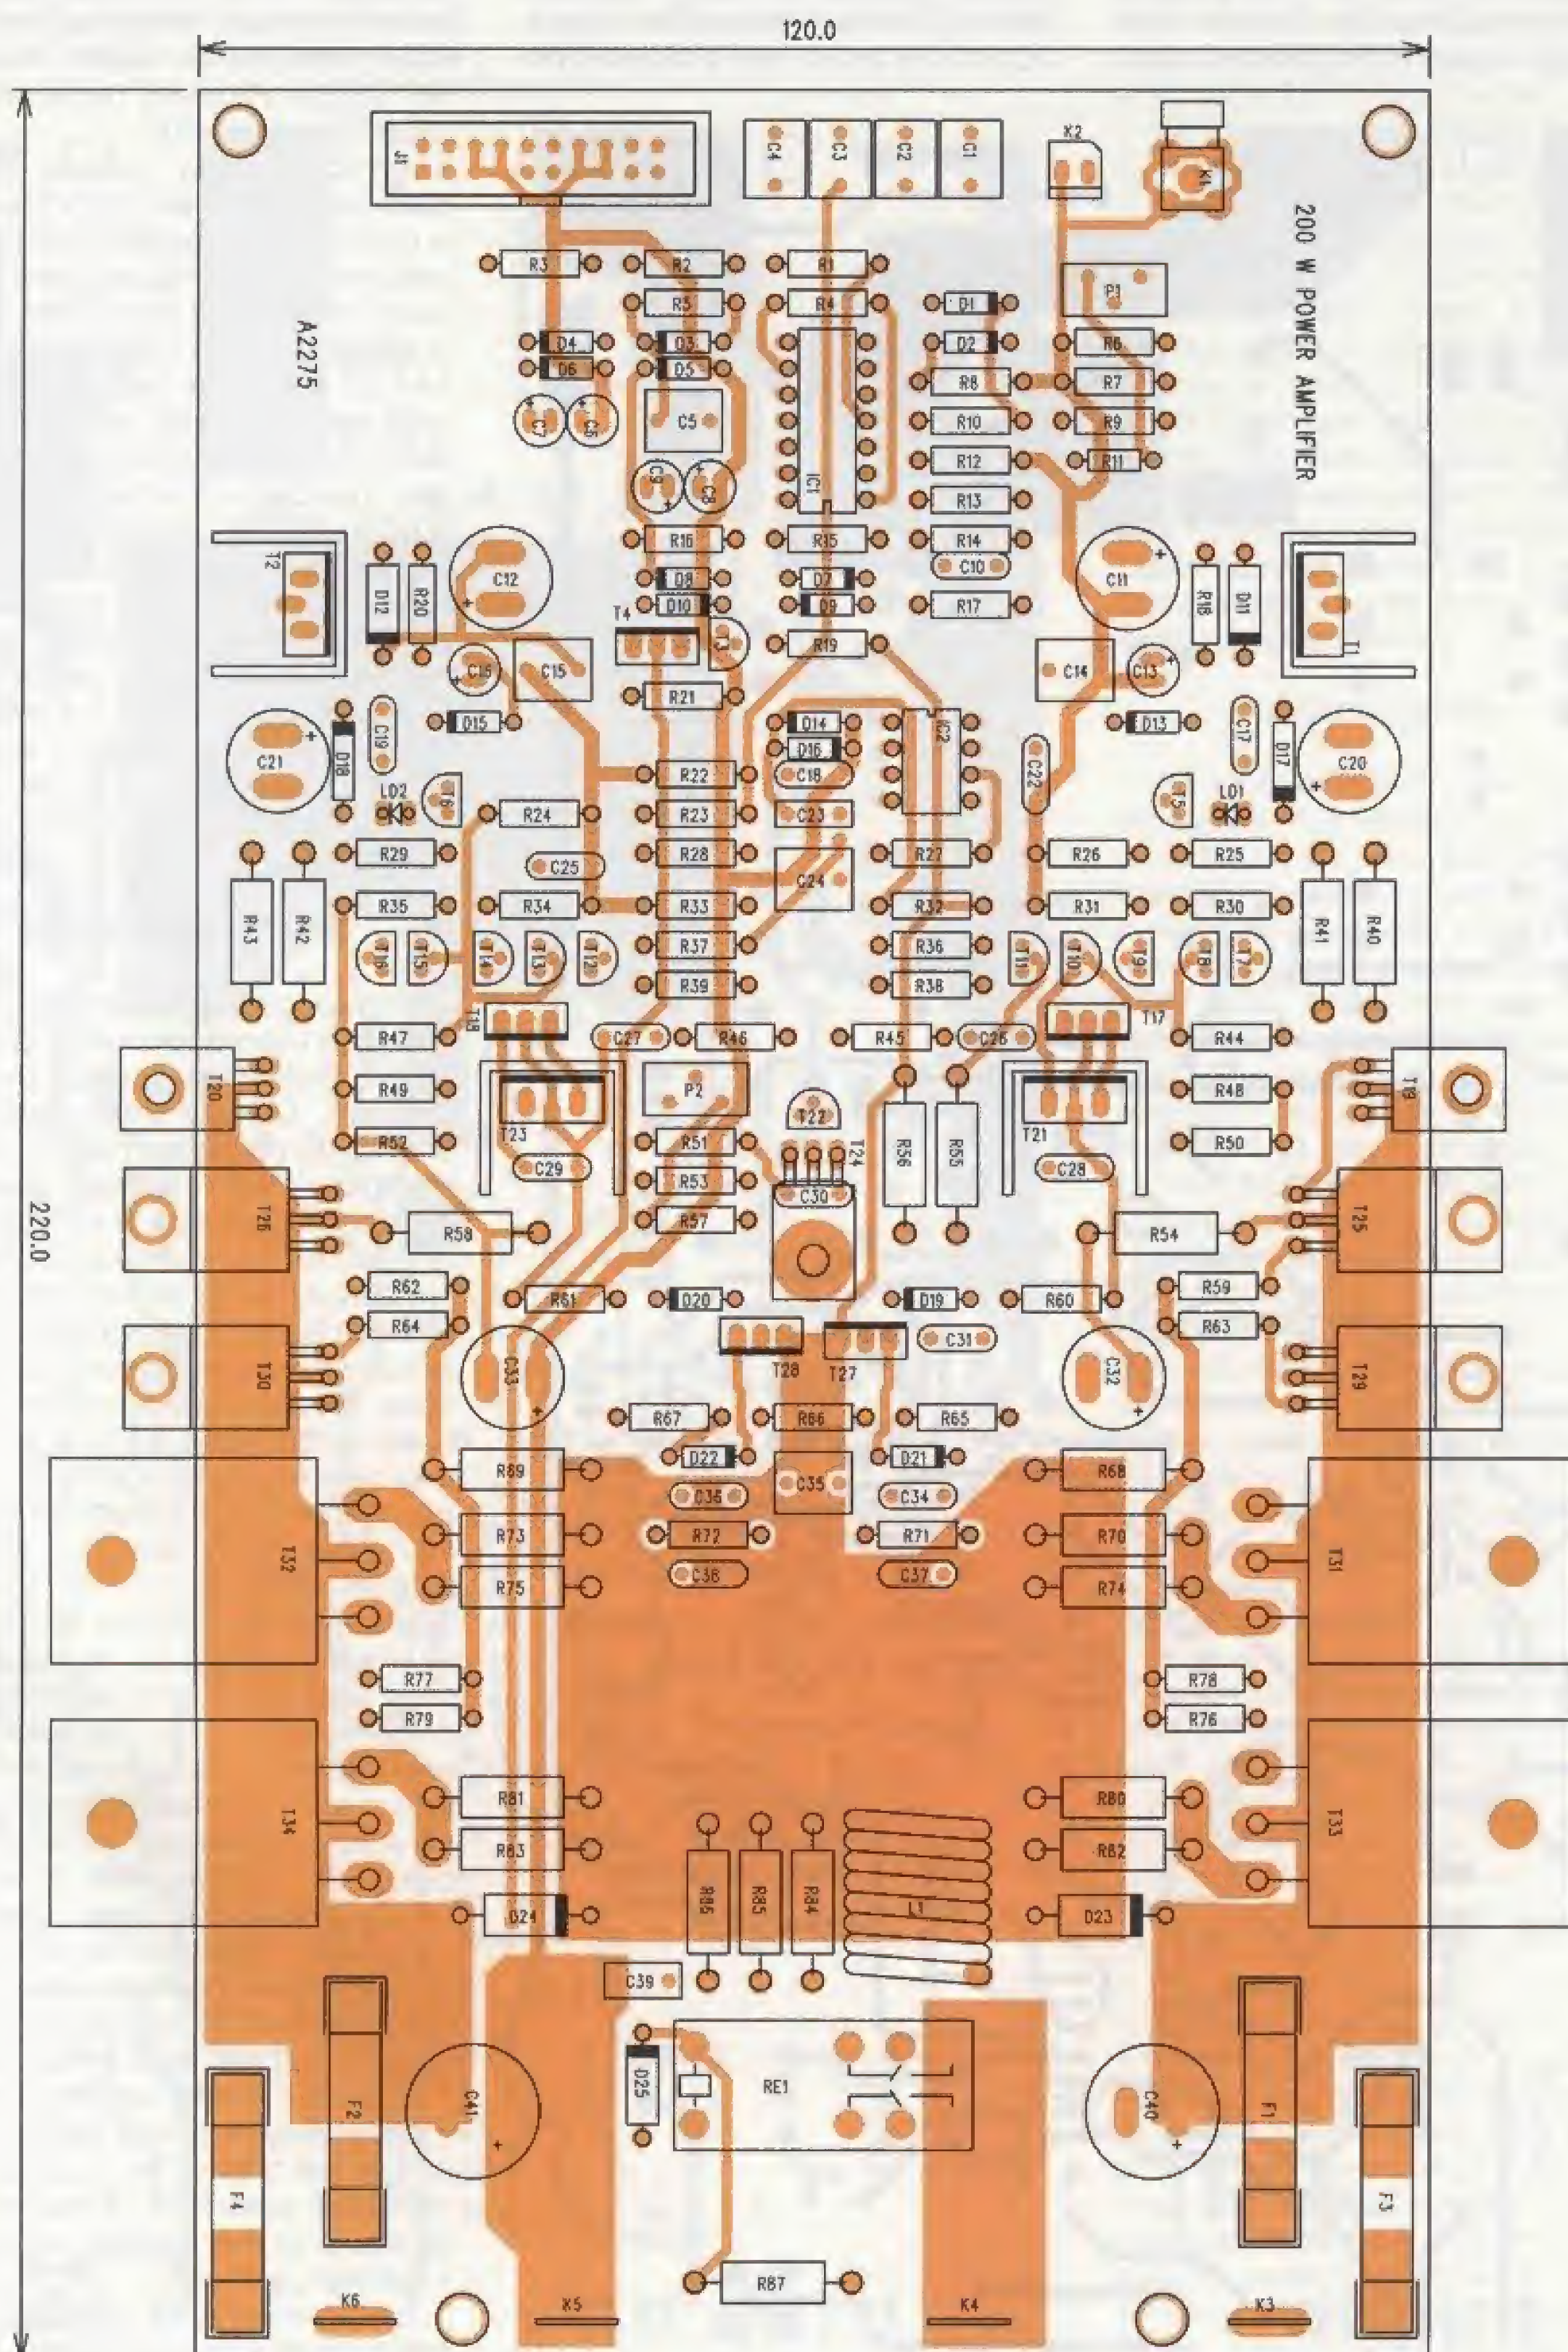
Deska spojů ze strany spojů (BOTTOM)
